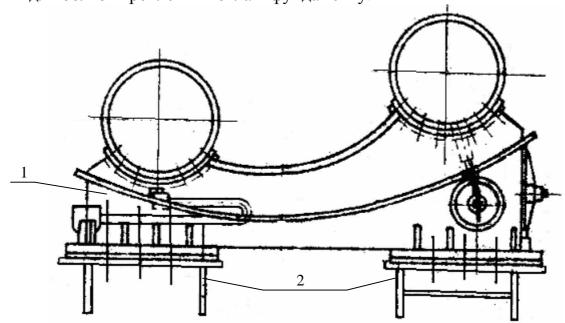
Крепление котла к переходным стульям фундамента: 1 – опорная рама; 2 – переходные стулья фундамента
